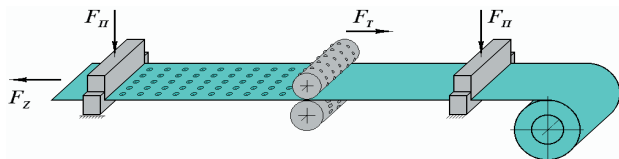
Способ изготовления рифленых профилей со сфероидальными выступами
